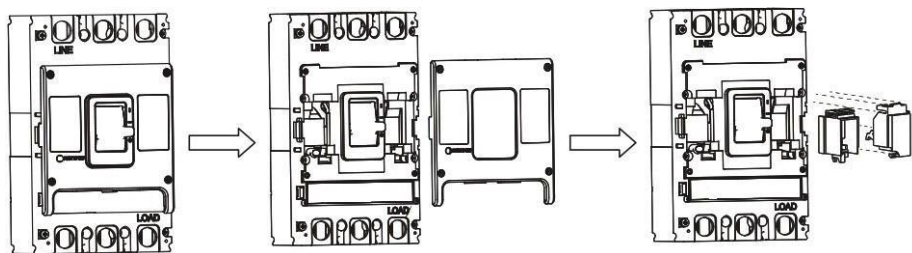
Схема установки аксессуаров внутрь корпуса аппарата
